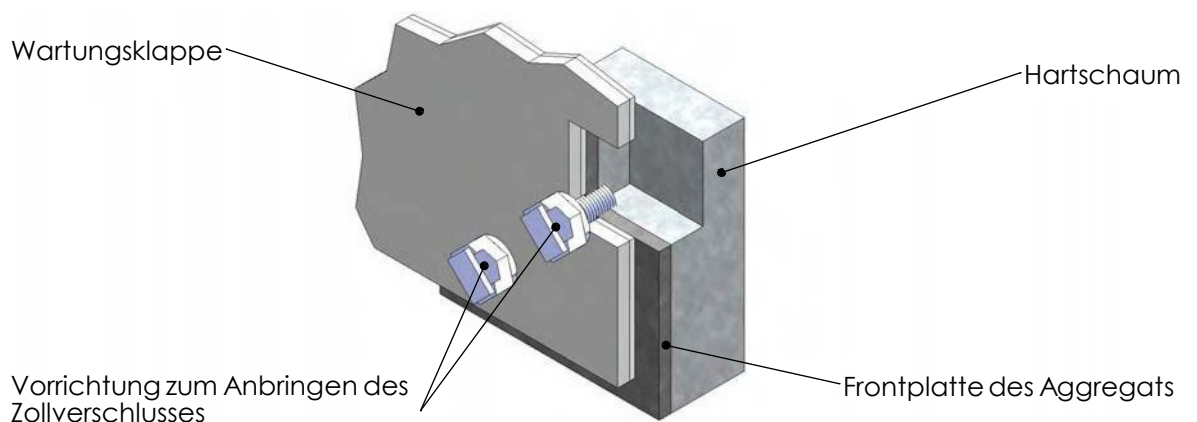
Zollverschlussvorrichtung (Schraubenköpfe)
